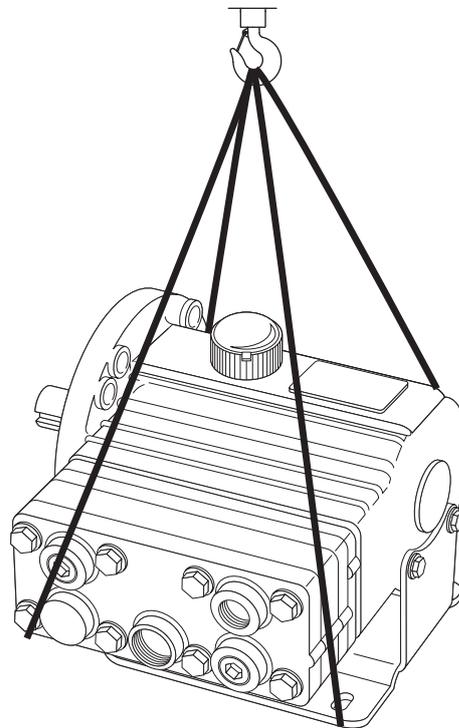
Hebezeug befestigen an Pumpe (Beispiel 1)
